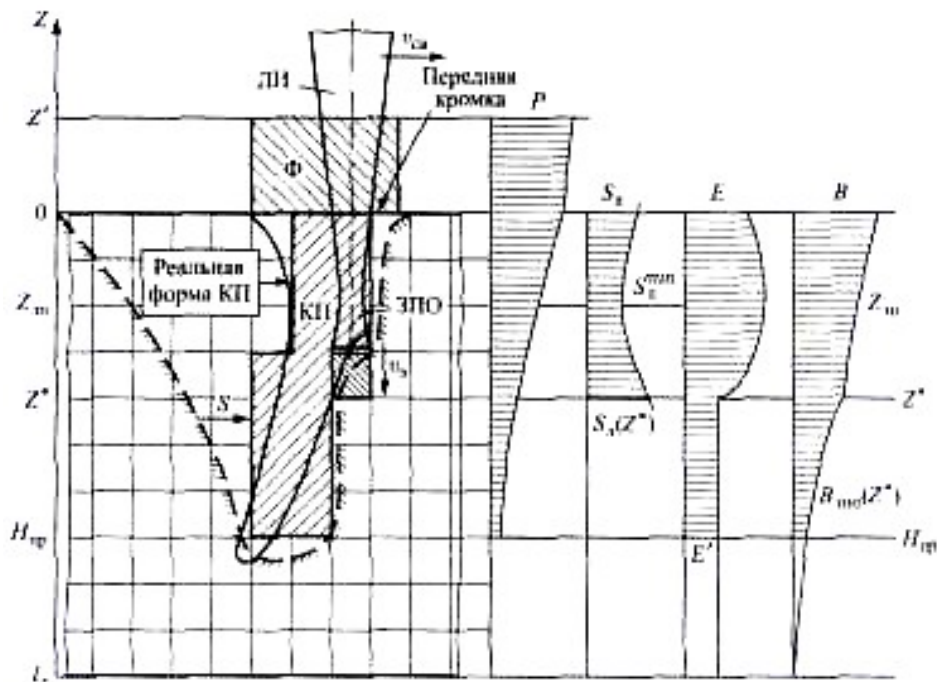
Модель лазерной сварки в режиме глубокого проплавления
